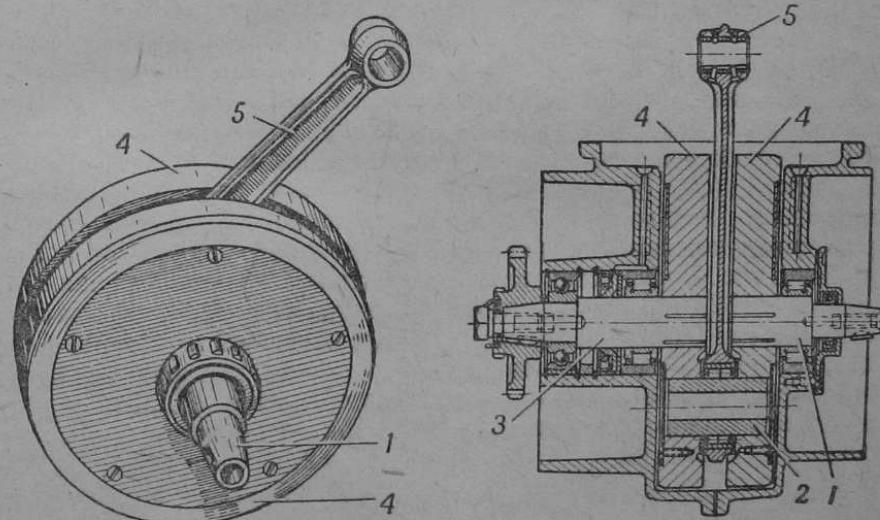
Коленчатый вал двигателя ИЖ-49:
